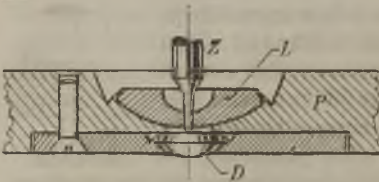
Zapfenlager mit Loch- und Deckstein.
